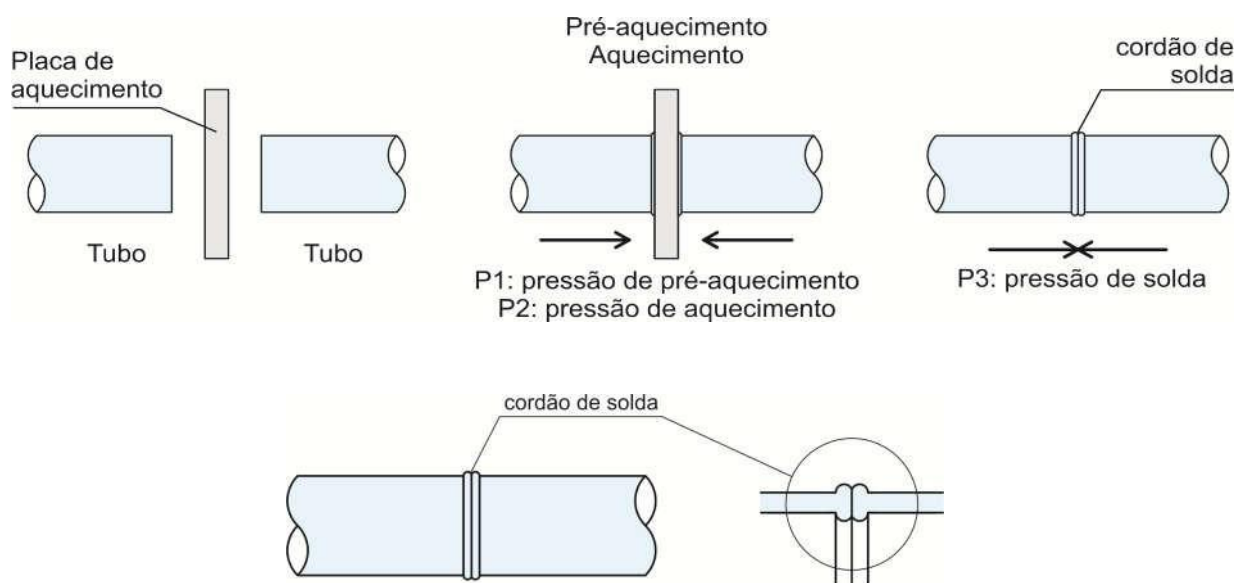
Faseamento da soldadura topo a topo em tubagens de PEAD
